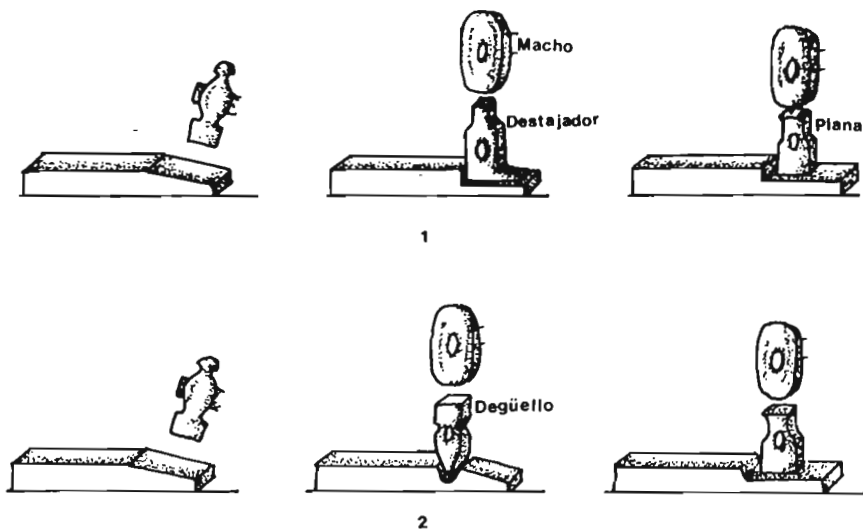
Rebajado angular; 2. Rebajado curvo.
